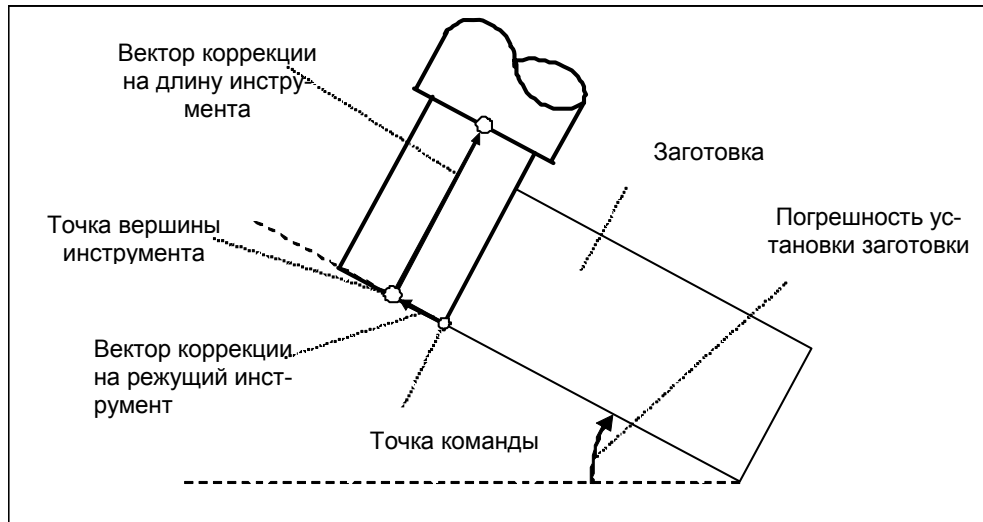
(m) Коррекция на режущий инструмент, когда имеется погрешность установки заготовки (если RCM=1)
